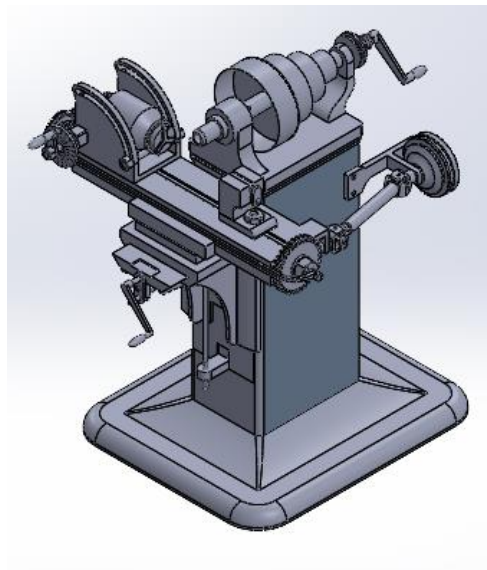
Fresadora Universal de Frederick W. Howe en SolidWorks.
